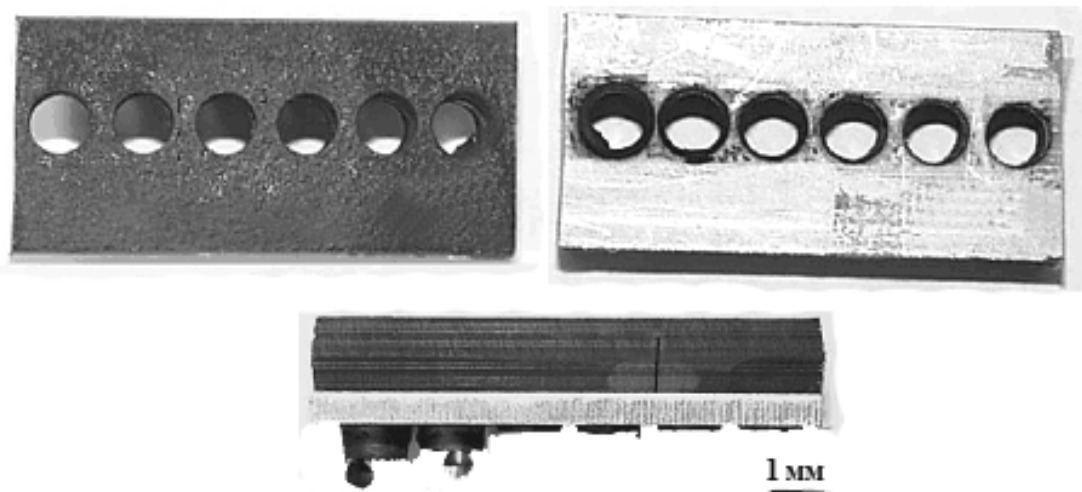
Виды сверлу, снизу и сбоку на пакет КМУ/Тi
